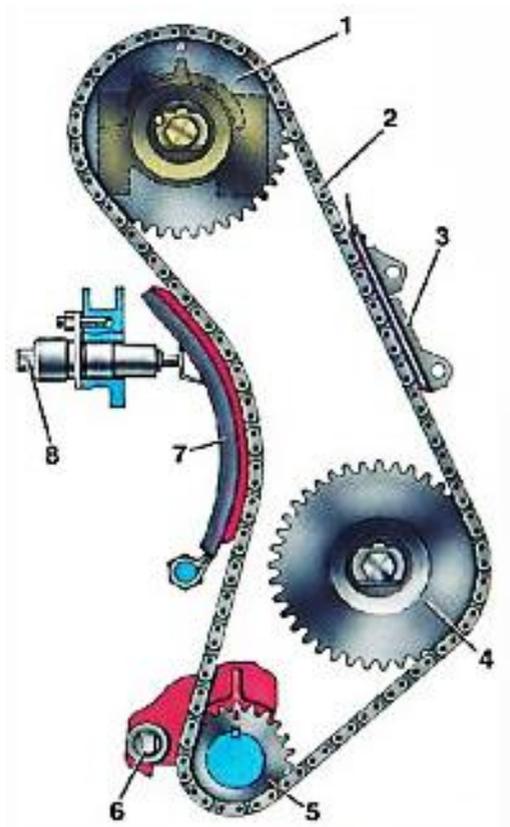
Схема механизма привода распределительного вала и вспомогательных агрегатов:
